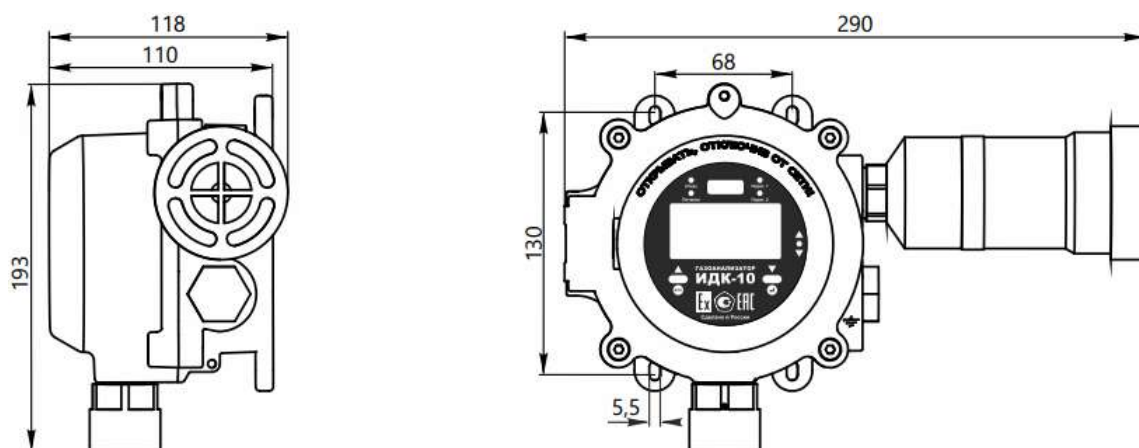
Габаритный чертеж ИДК-10-01 с ОСЗВ, защитным козырьком и крепежом на горизонтальную поверхность
